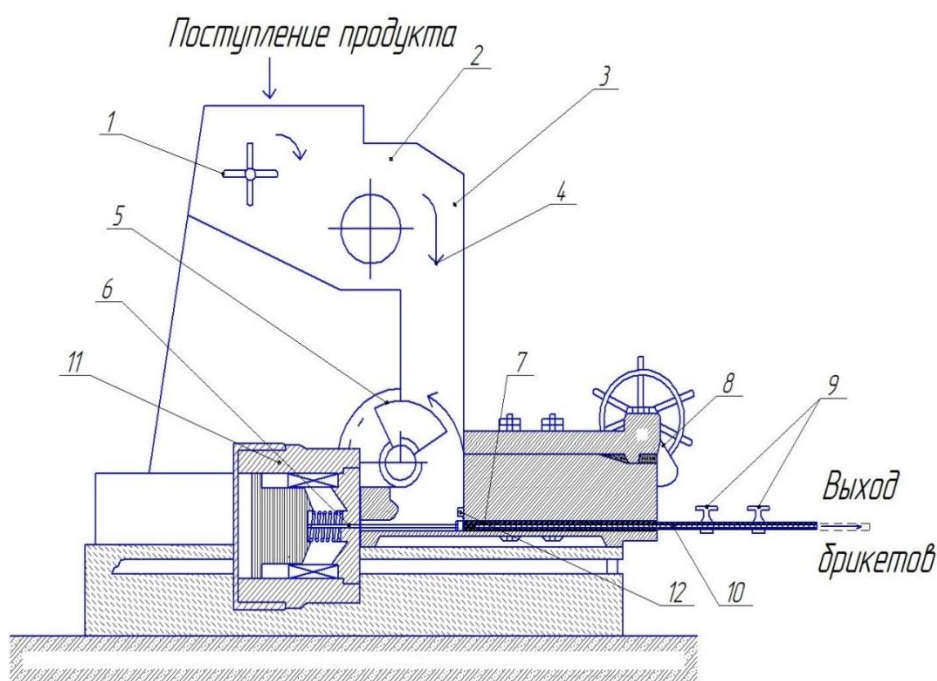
Технологическая схема штокового пресса ШП-1 с приводом от ЛЭМД: 1 - Разрыхлитель; 2 - Питающий механизм; 3 - Питающий валик; 4 – Канал; 5 - Подпрессователь; 6 – Шток-пуансон; 7 – Прессовая камера; 8 – Механизм для регулирования брикета; 9 – Нажимные механизмы; 10 – Мундштук; 11 – Линейный электромагнитный двигатель; 12 – Датчик, отвечающий за остановку штока-пуансона в конце рабочего хода
